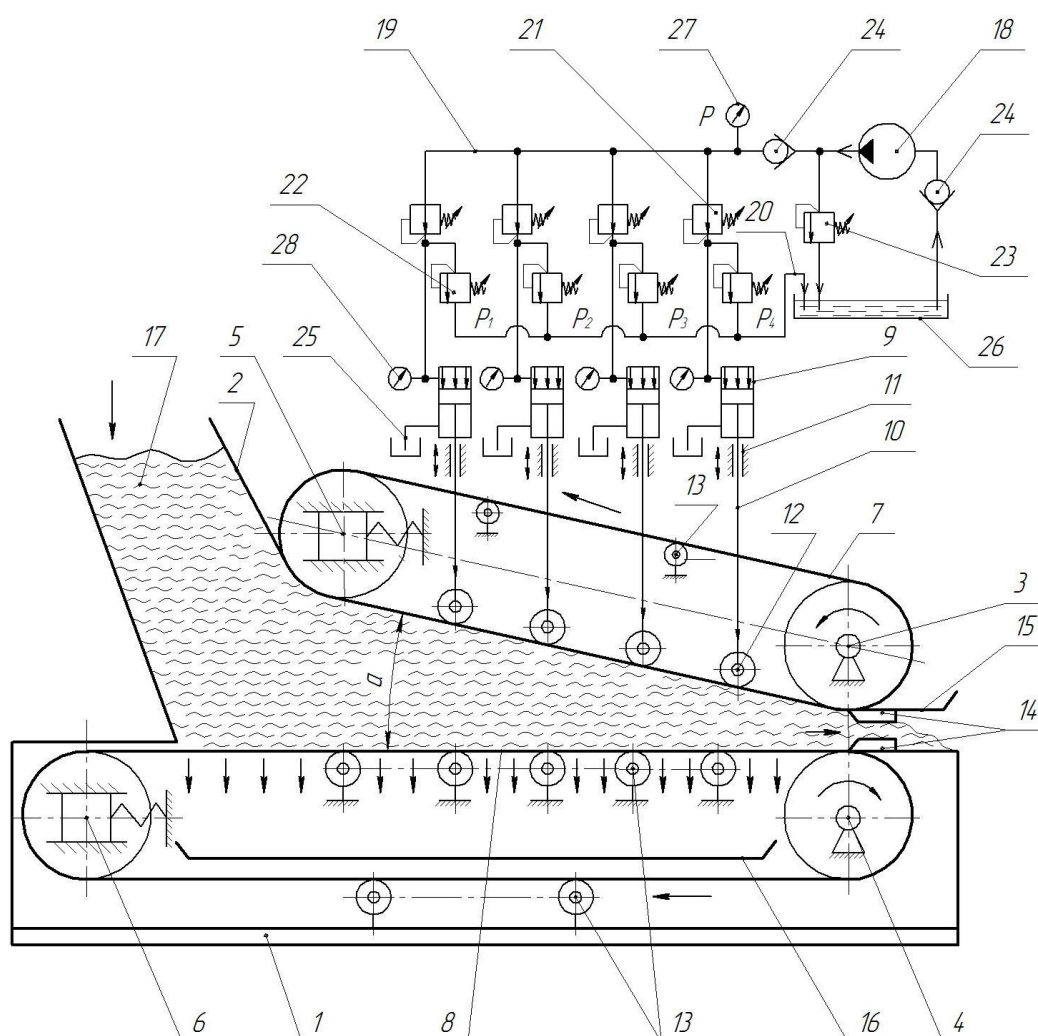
Общий вид ленточного фильтр-пресса непрерывного действия
